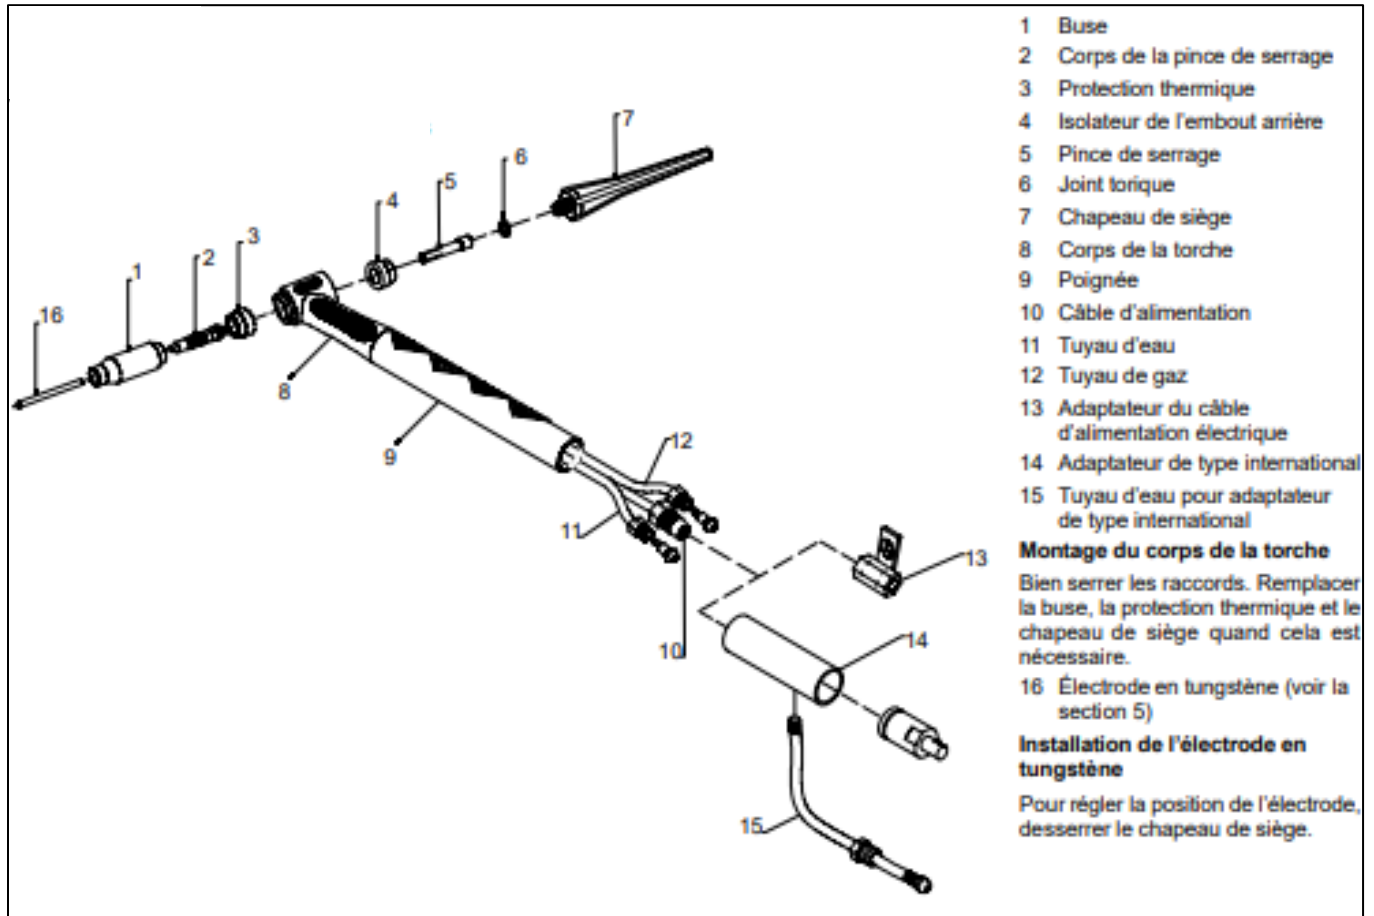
schéma de composants de la torche de soudage [31].
